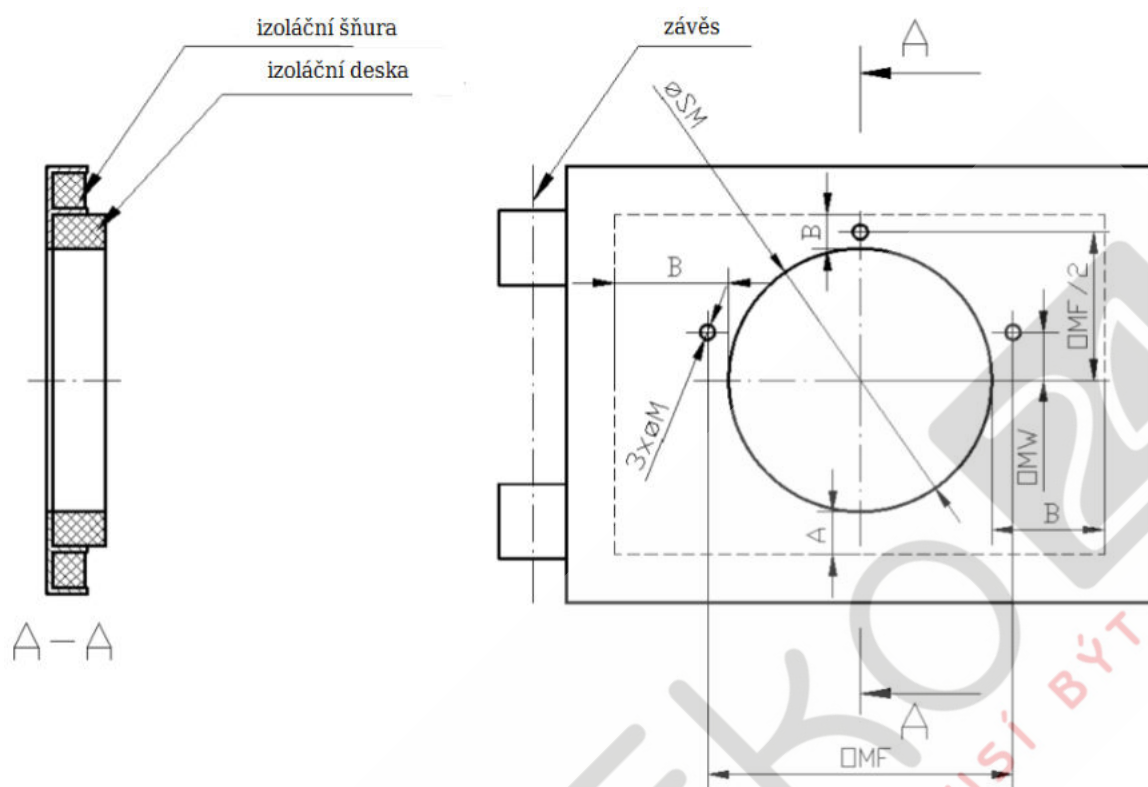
Schéma vytváření montážních otvorů pro hořáky: 4-16 kW, 5-20 kW, 6-26 kW, 8-36 kW, 10-50 kW.
